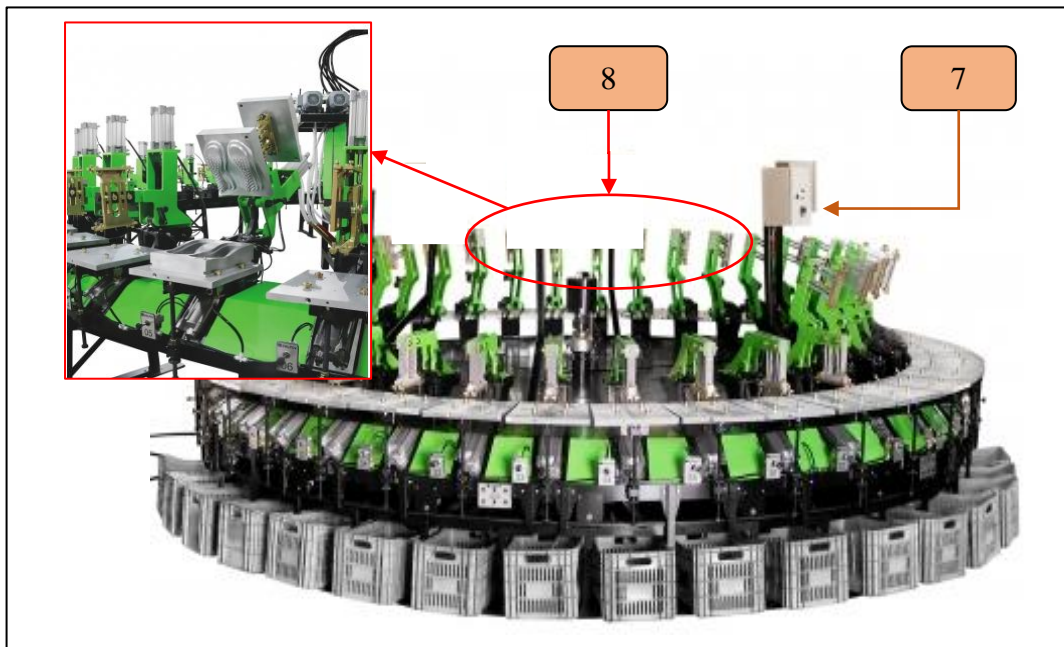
Conjunto de sistemas de la máquina inyectora [30].
